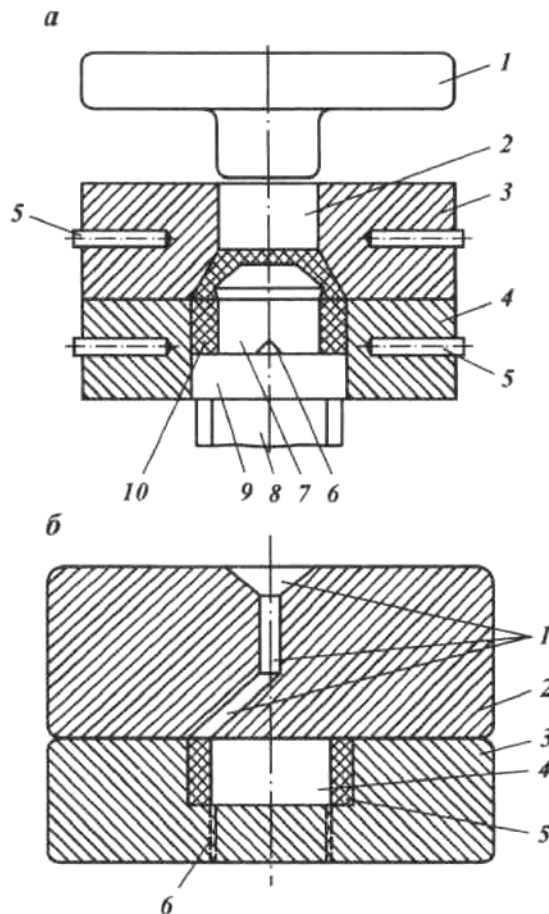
Схемы пресс-форм для нанесения полимерных покрытий:
